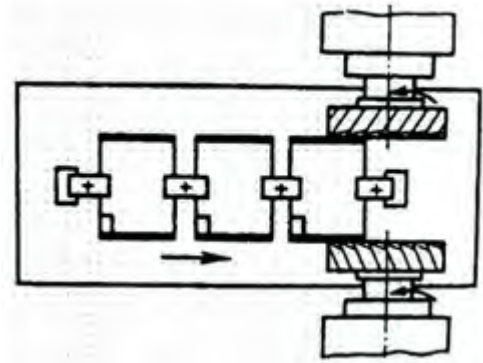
Комбіноване фрезерування на повздовжньо-фрезерному верстаті
